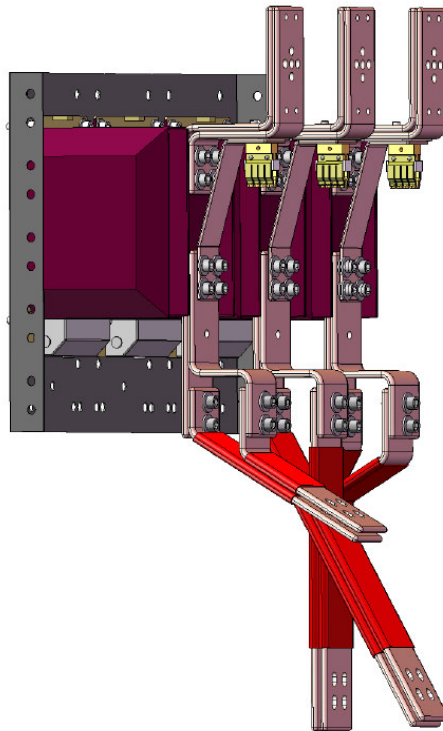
Preassemblaggio TA con congiuntore e collegamento per il sezionatore di terra
